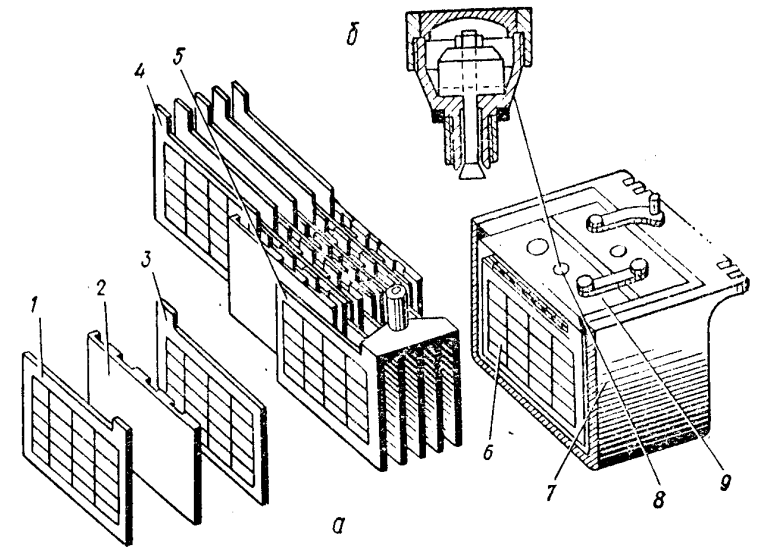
Конструкция аккумуляторной батареи и рабочей пробки
